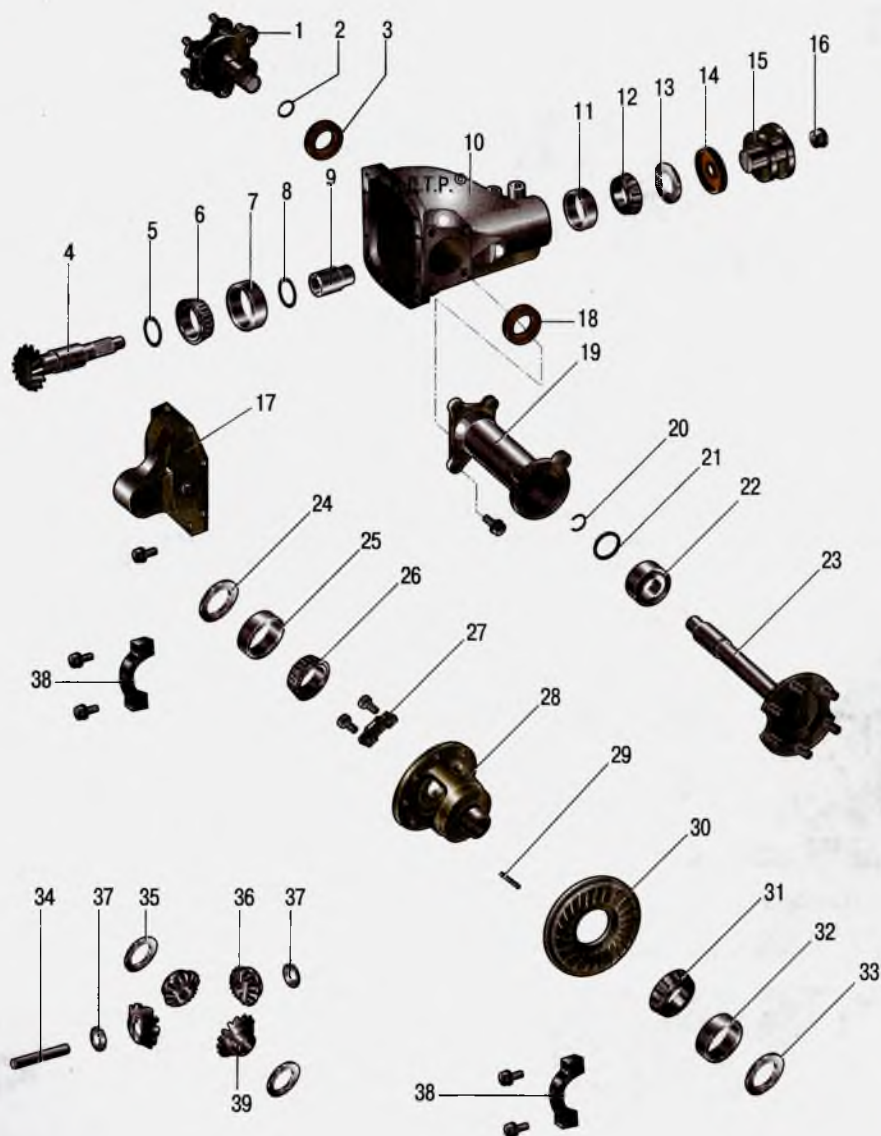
Детали редуктора привода передних колес: 1 – правая полуось; 2, 20 – стопорное кольцо; 3, 18 – сальник полуоси; 4 – ведущая шестерня главной передачи; 5, 8, 24, 33 – регулировочная шайба; 6, 7 – подшипник; 9 – кожух; 10 – картер редуктора привода передних колес; 11, 12 – подшипник; 13 – маслоотражатель; 14 – сальник; 15 – фланец с пыльником; 16 – гайка; 17 – крышка редуктора привода передних колес; 19 – корпус левой полуоси; 21 – фиксирующее кольцо; 22 – подшипник; 23 – левая полуось; 25, 26, 31, 32 – подшипник; 27 – стопорная пластина; 28 – корпус дифференциала; 29 – шпилька; 30 – ведомая шестерня главной передачи; 34 – ось сателлитов; 35 – упорная шайба шестерни полуоси; 36 – сателлит; 37 – упорная шайба сателлита; 38 – крышка подшипника; 39 – шестерня полуоси
